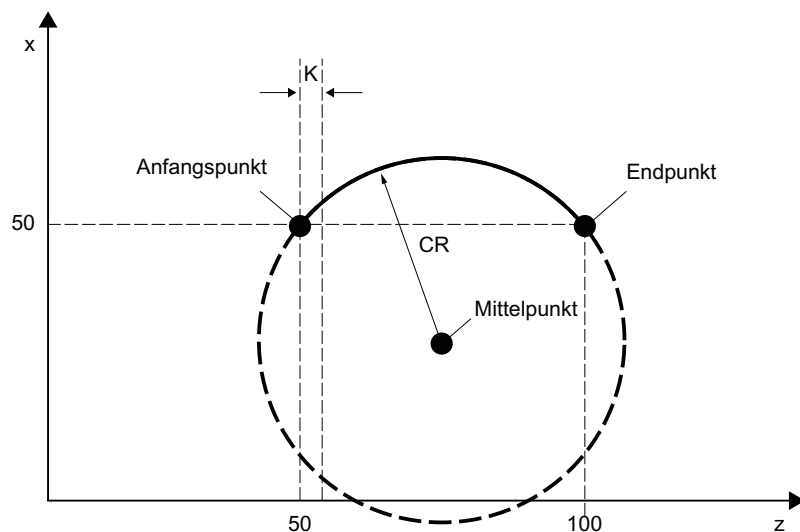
Balliges Gewinde im Uhrzeigersinn mit Endpunkt- und Radiusprogrammierung
